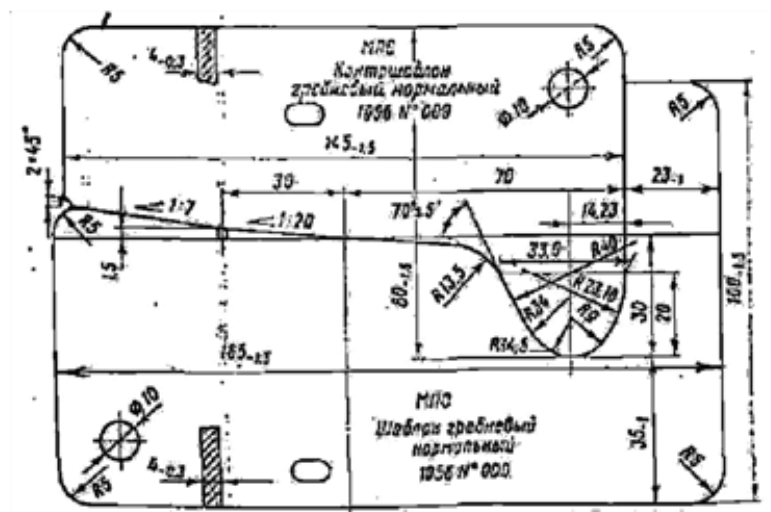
Шаблон и контршаблон для проверки профиля гребня и поверхности катания
